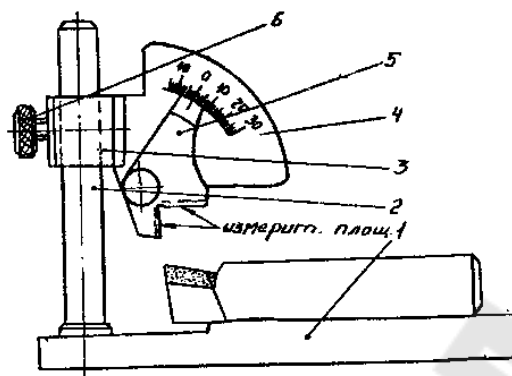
Резцовый угломер: 1 – плита, 2- вертикальная стойка, 3 – блок состоящий из трех шкал с измерительными линейками, 4,5 шкальное устройство, 6- фиксатор
